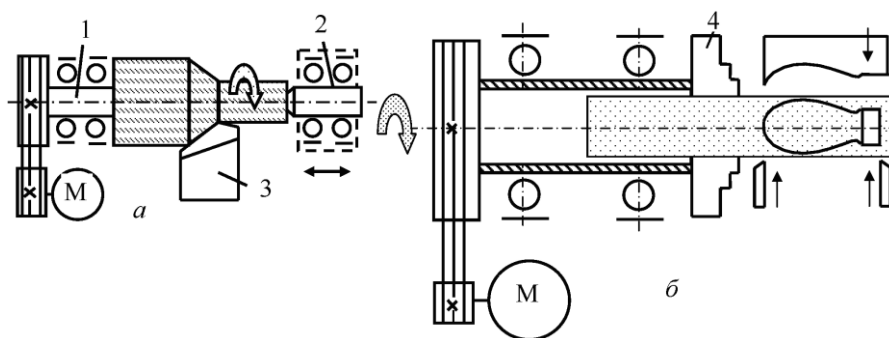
Обробка деталей: *а* - в центрах; *б* - в патроні
